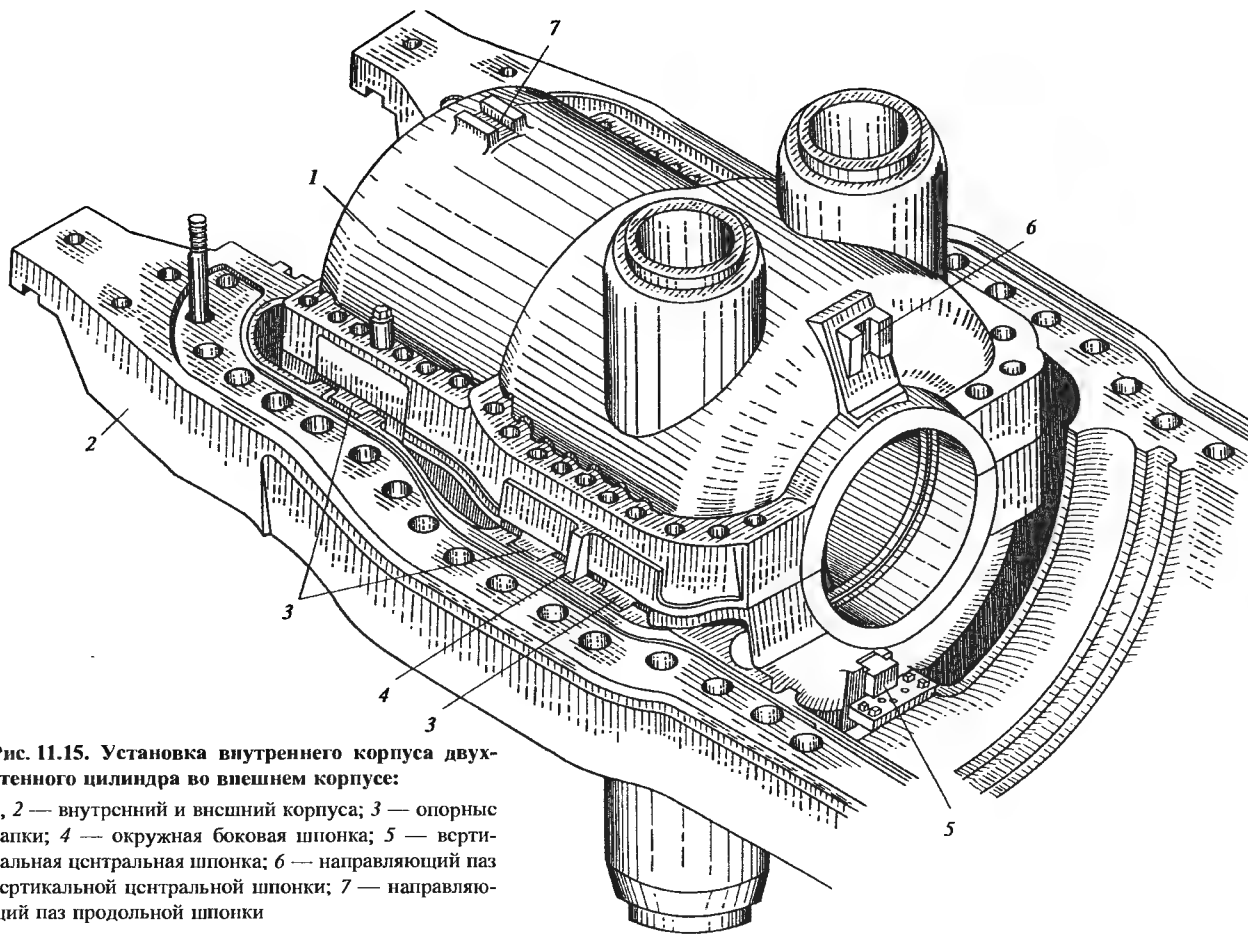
Установка внутреннего корпуса двухстенного цилиндра во внешнем корпусе:
